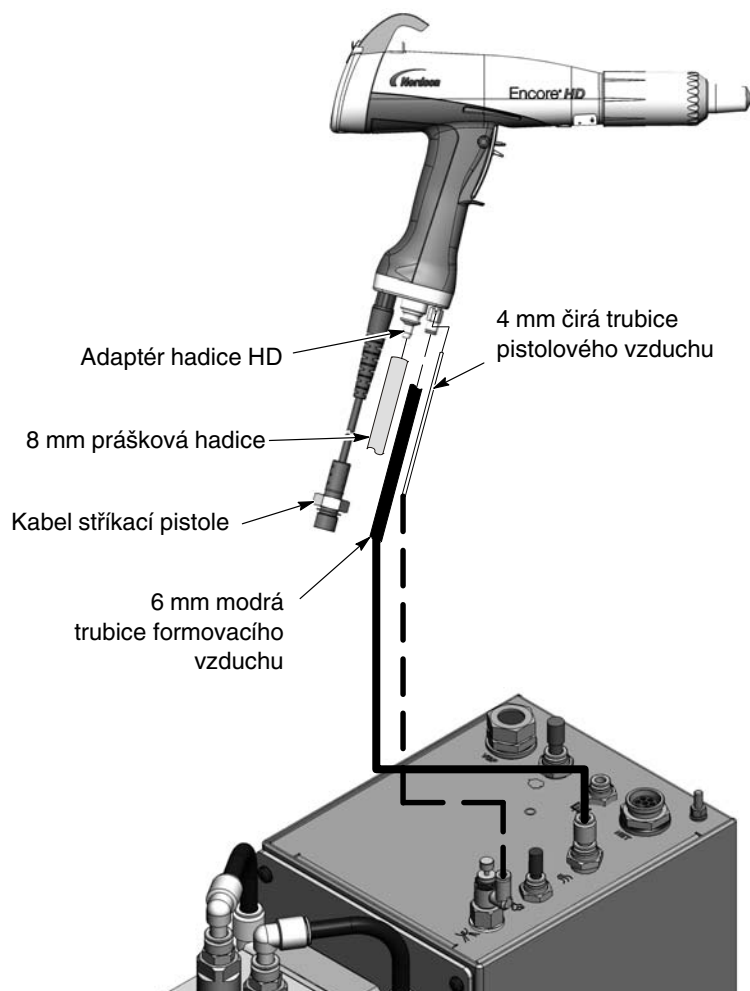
Připojení kabelu stříkací pistole k řídicí jednotce systému – zobrazen mobilní systém
